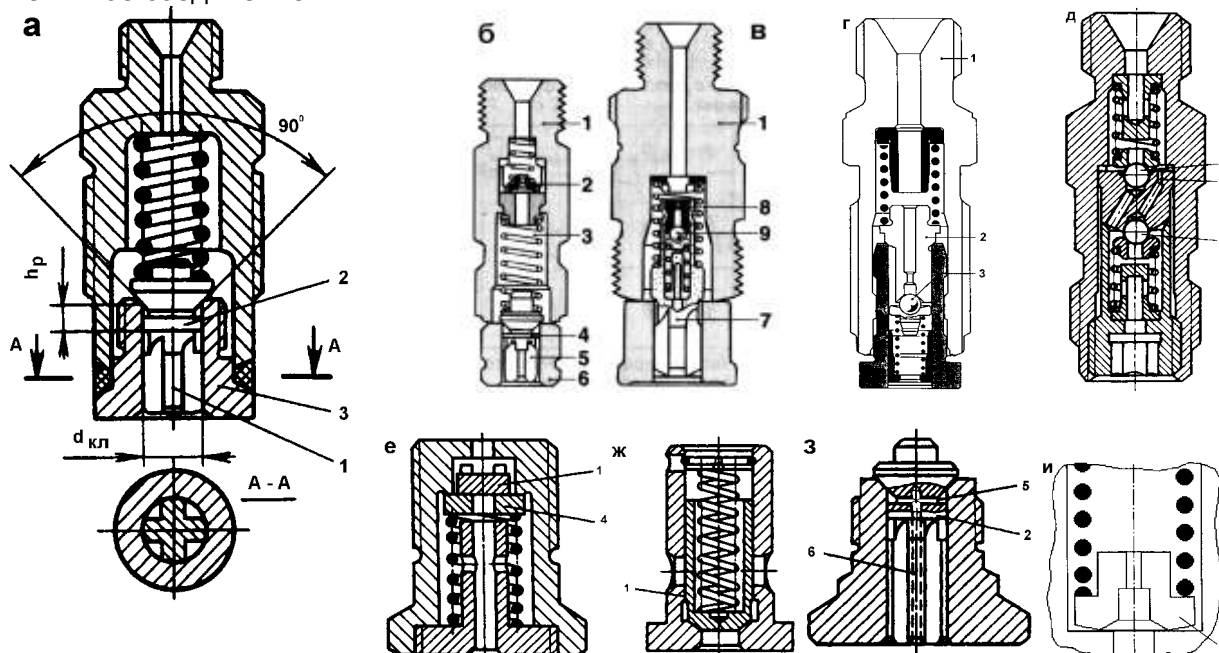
Нагнетательные клапаны ТНВД: 1 - нагнетательный клапан; 2 - разгружающий пояс; 3 - седло клапана; 4 - реверсивный клапан для подавления волны давления; 5 - жиклер; 6 - каналы клапана-корректора; 7 - последовательный клапан.
